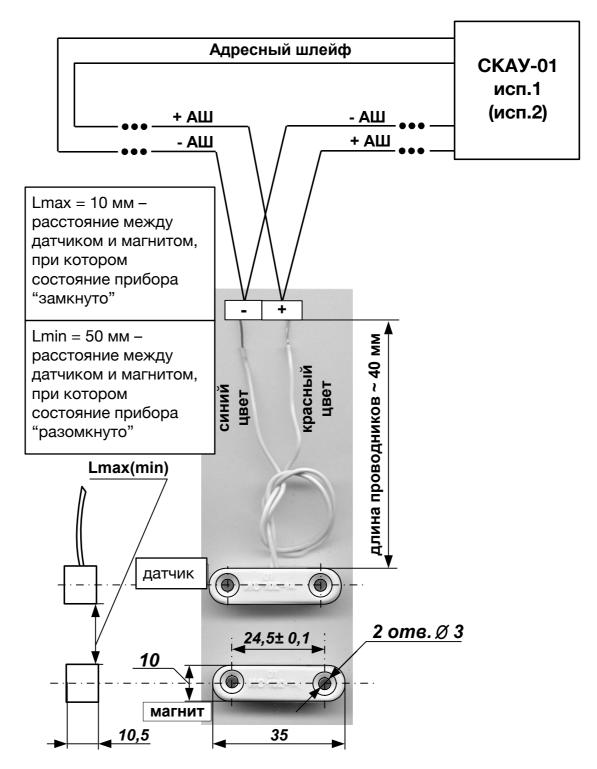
Конструкция, подключение, габаритные и присоединительные размеры
